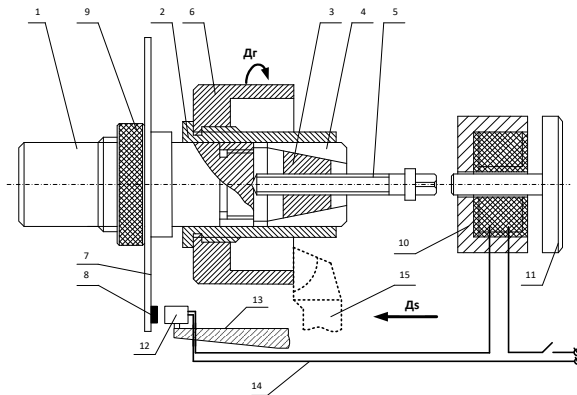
Приспособление для мгновенного прекращения резания: 1- корпус; 2 – втулка; 3 – конус; 4 – цапга; 5 – винт; 6 – образец; 7 – диск; 8 – магнит постоянный; 9 – контргайка; 10 – электромагнит; 11 - сердечник электромагнита; 12 – геркон; 13 – штанга; 14 – электрическая цепь; 15 - резец.
